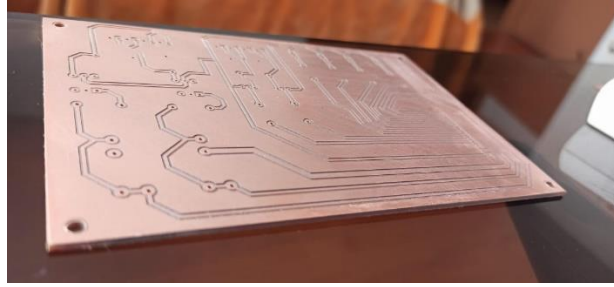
Fabricación de placa de actuadores en máquina CNC
